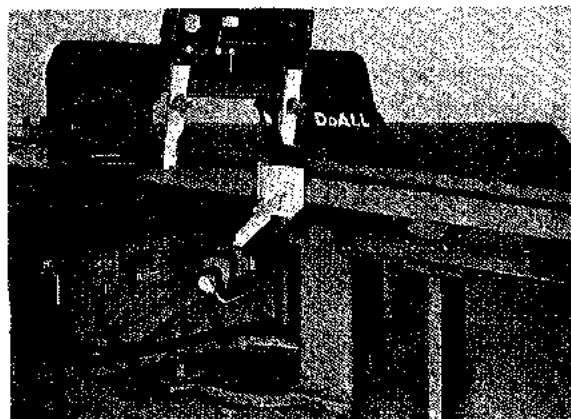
Sierra de cinta horizontal para tronzar según un ángulo (DoAll Co.)
